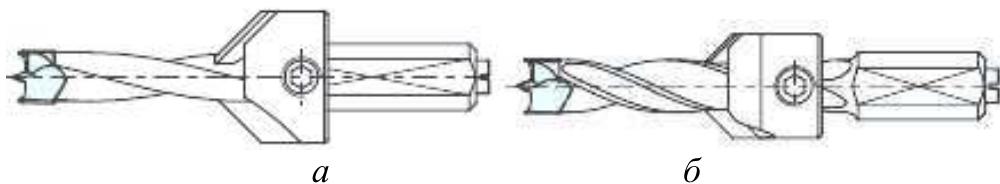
Сверла для сверления глухих отверстий: без направляющей ленточки (а) и с направляющей ленточкой (б)
